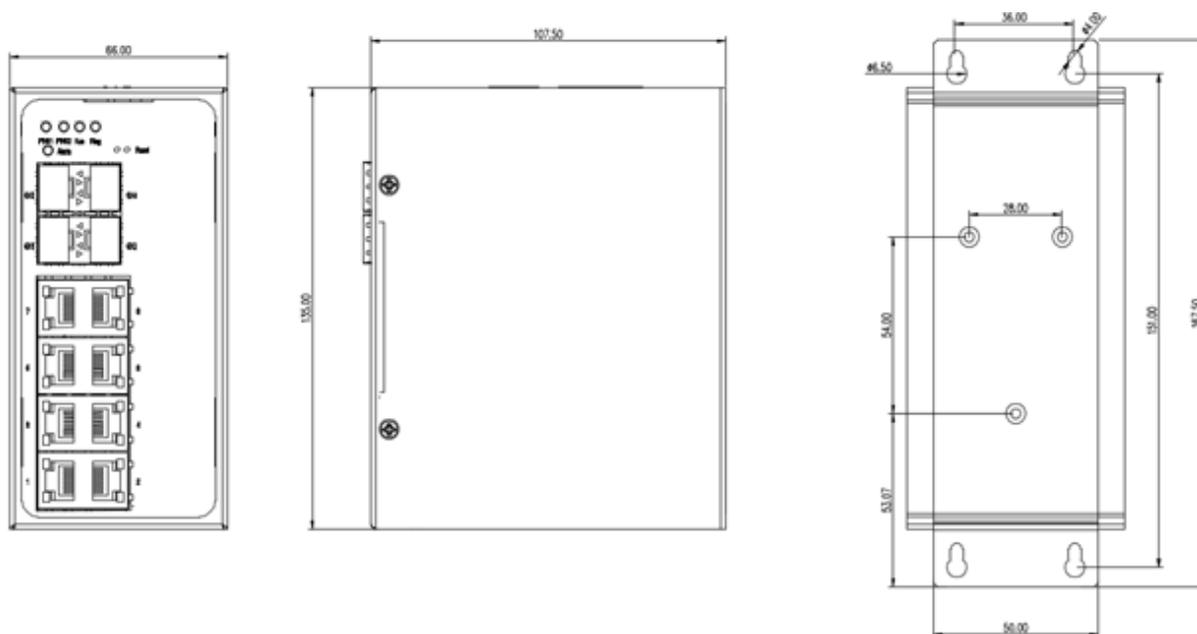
Габаритный чертеж корпуса «Тип 1» с креплением на плоскую поверхность
